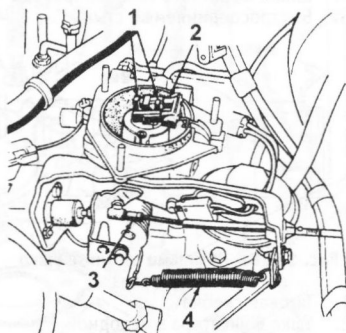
Чтобы отсоединить разъем инжектора на автомобилях с СВКД, сожмите шпонки и поднимите
